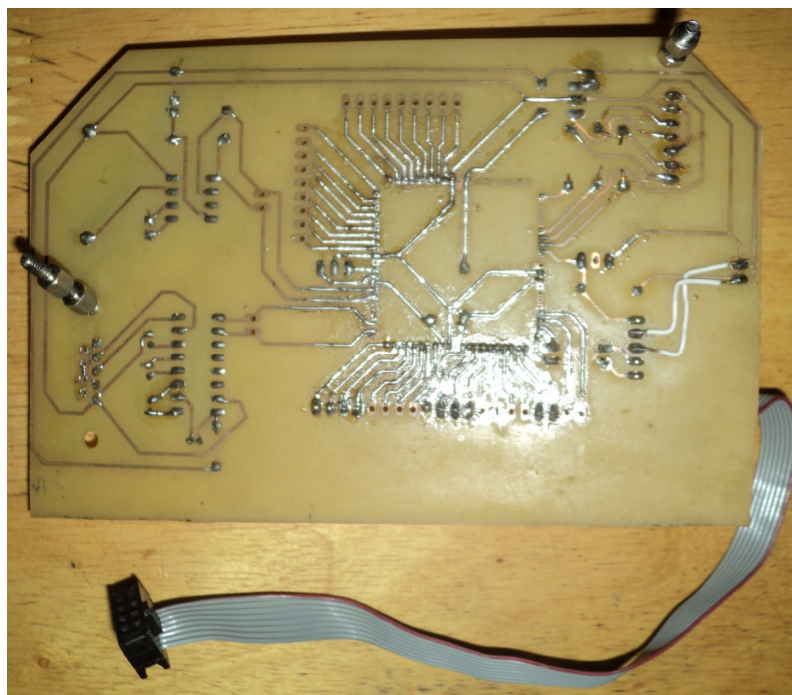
Vista real de la parte frontal de la tarjeta de adquisición
